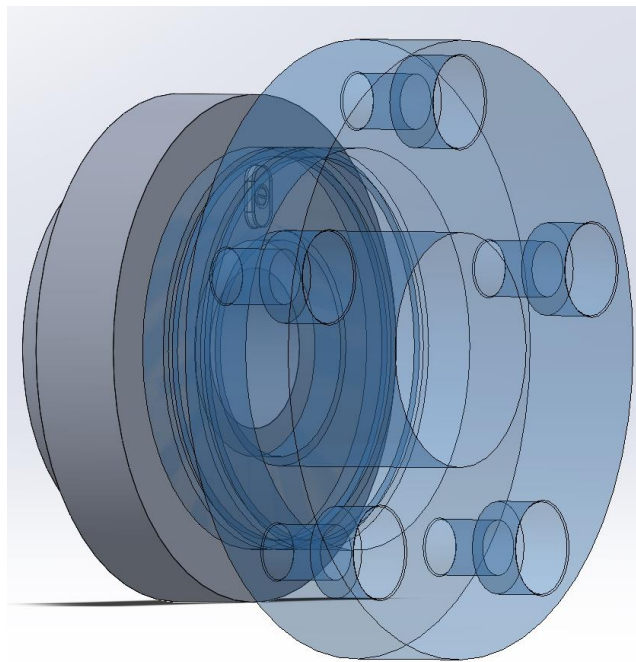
Montagem da tampa de pré-carga com o espaçador com a chaveta de maior dimensão
